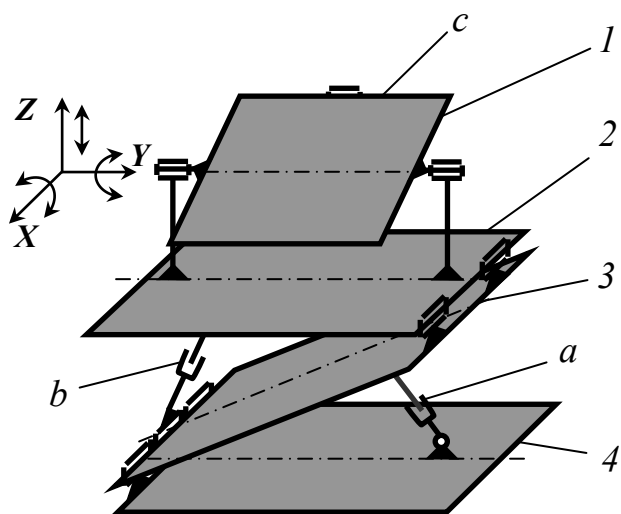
Расчетная схема оригинальной части пространственного манипулятора: 1- установочное звено (рабочий стол); 2- опорно-поворотное устройство; 3- наклонная платформа; 4- поворотный стол; а, b, c- приводные устройства (ШВП, гидроцилиндры)
